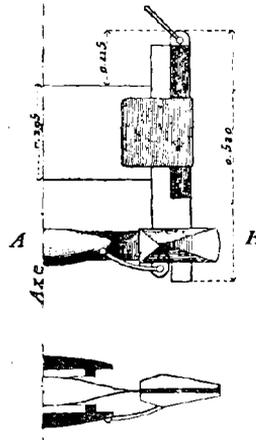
Appareil pour la prise de courant. Demi-plan et demi-élévation.
